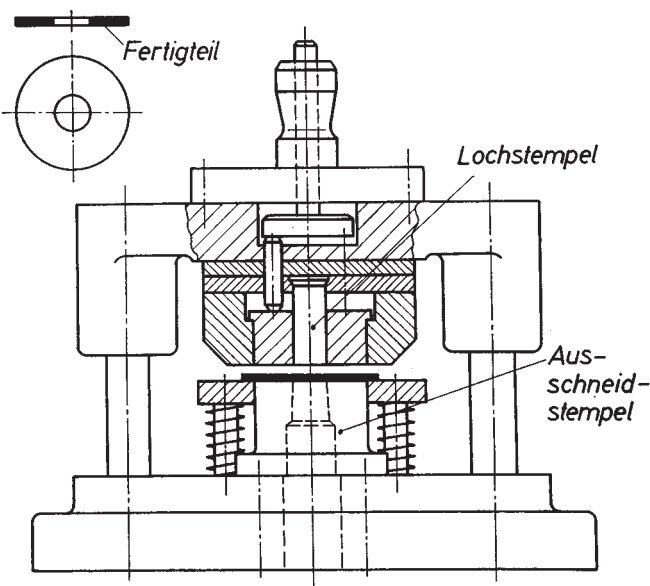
Gesamtschneidwerkzeug zum Lochen und Ausschneiden
